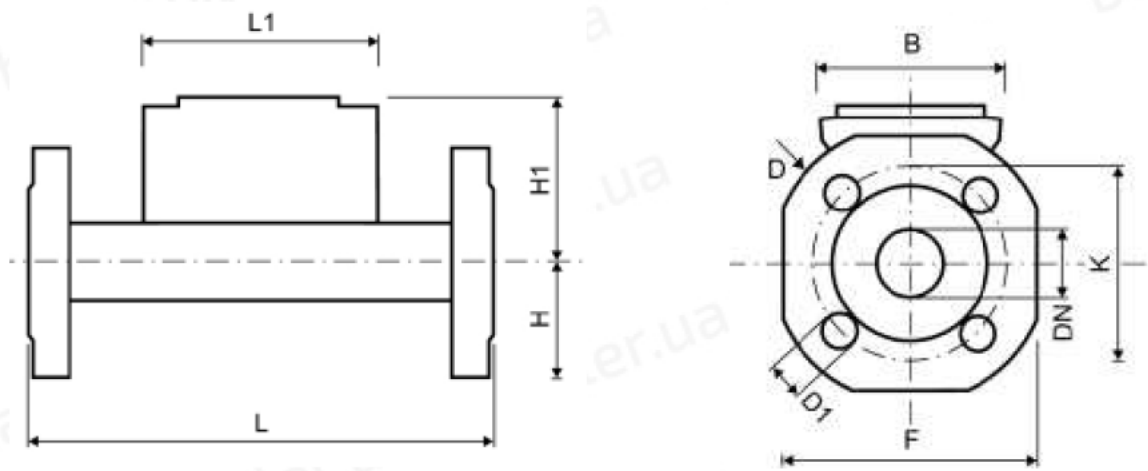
Габаритные размеры расходомера SHARKY FS 473 с фланцевым соединением
